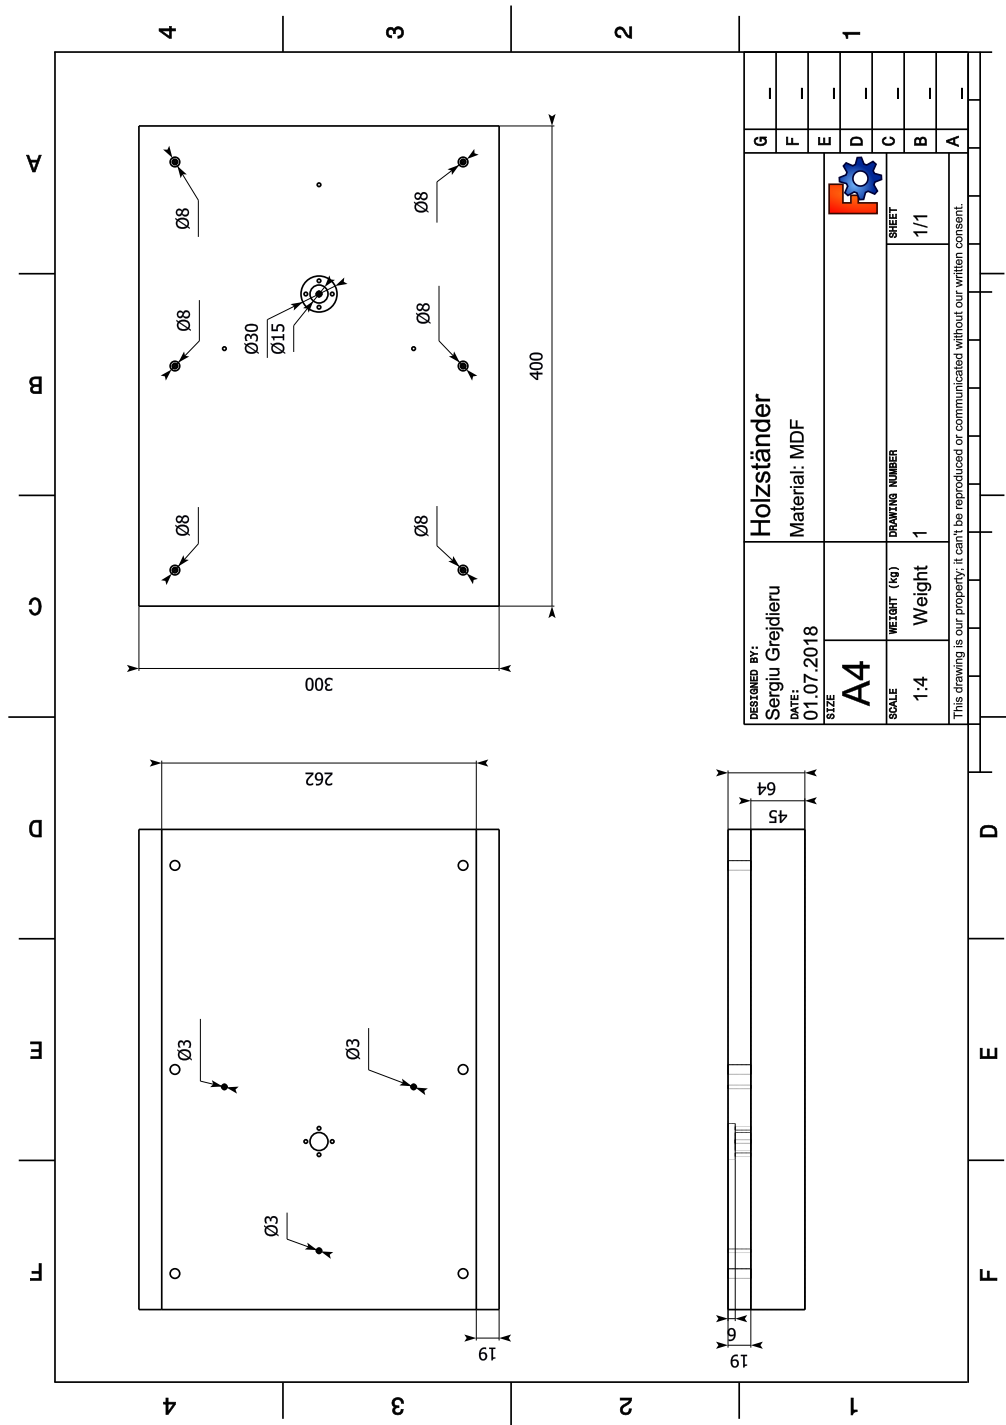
Technische Zeichnung: MDF Holzständer
